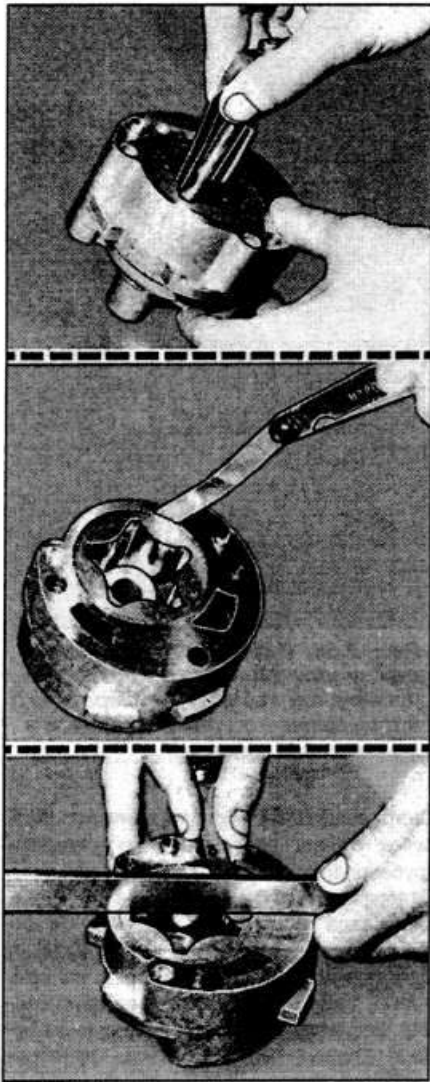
Вверху — проверка зазора между зубьями ведущей и ведомой шестерен; в середине — проверка зазора между наружным диаметром ведомой шестерни и корпусом насоса; внизу — проверка зазора между торцами шестерен и плоскостью корпуса насоса
